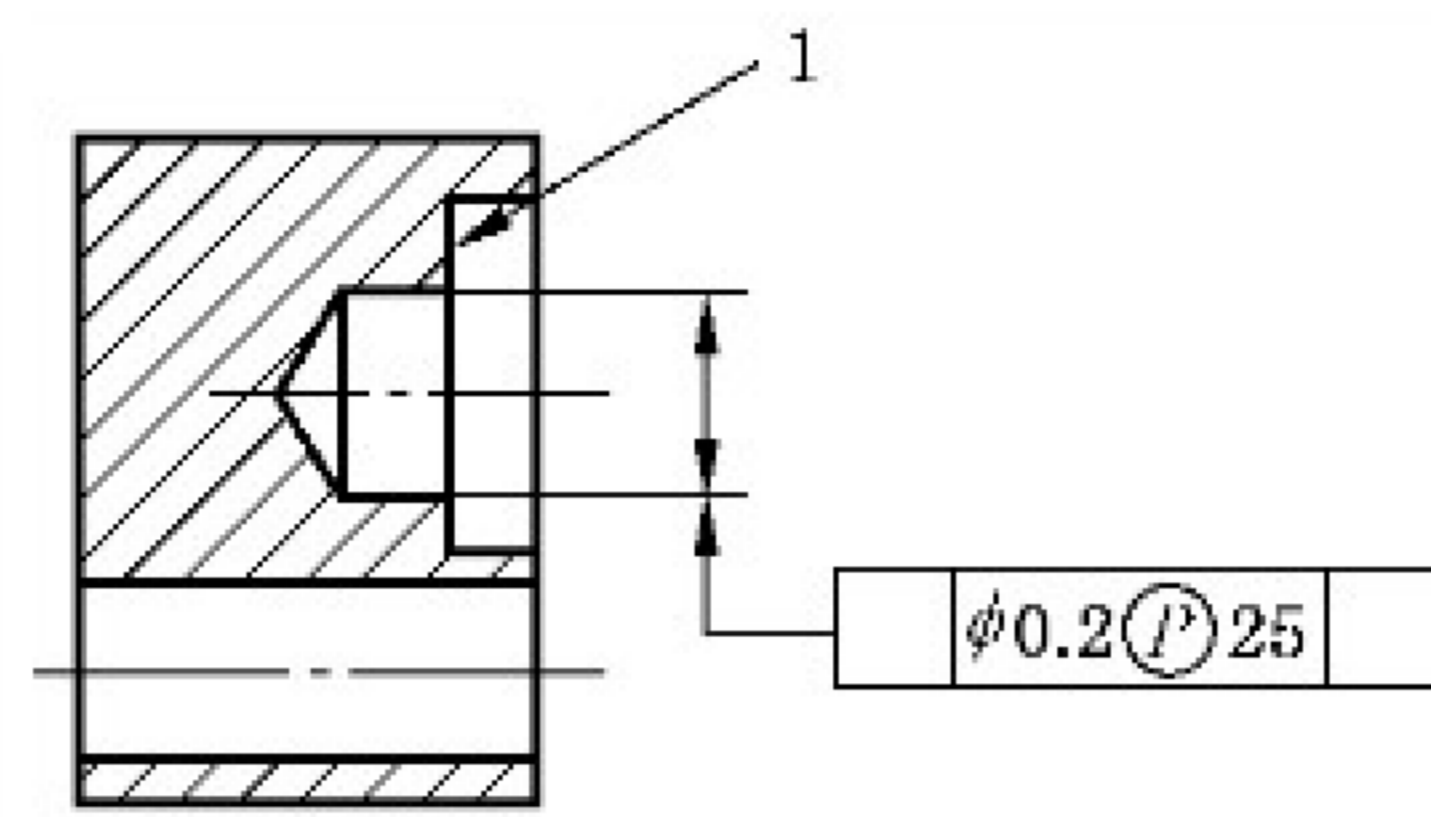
带延伸公差修饰符的几何公差规范标注,在公差框格中使用延伸被测要素长度来间接标注
